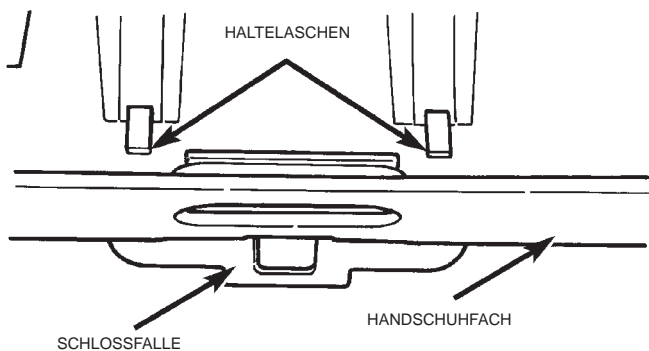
Schloßfalle des Handschuhfaches aus- und einbauen
